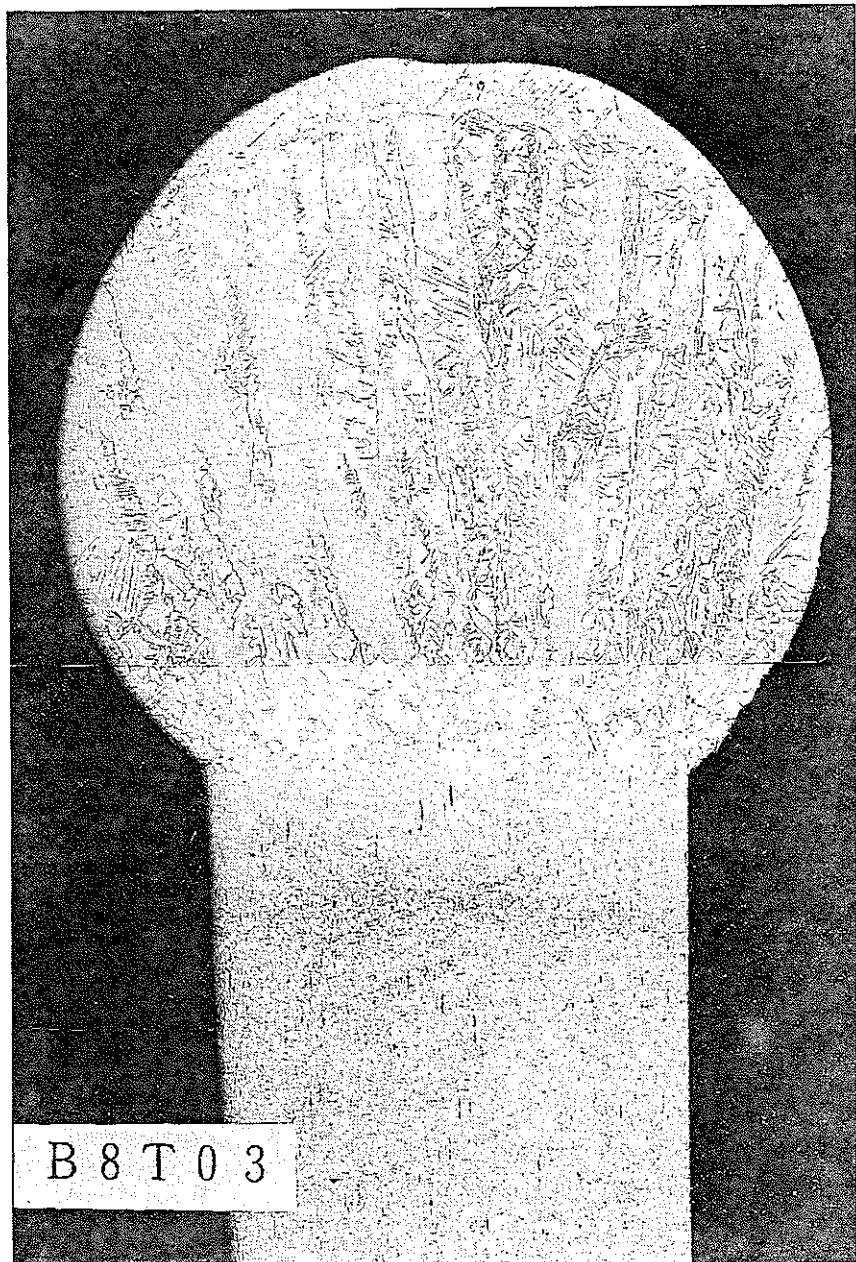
ワイヤ玉止溶接施行断面金相写真（上部）
